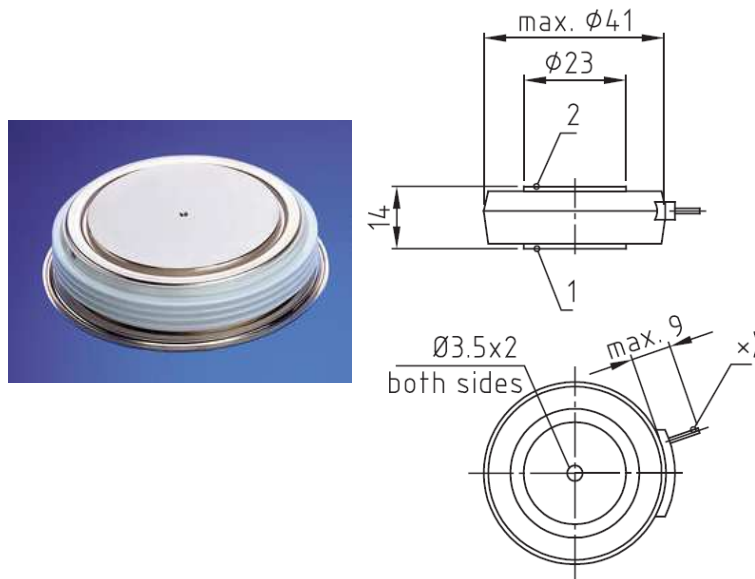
Dimensions et photo d'un boîtier press-pack
